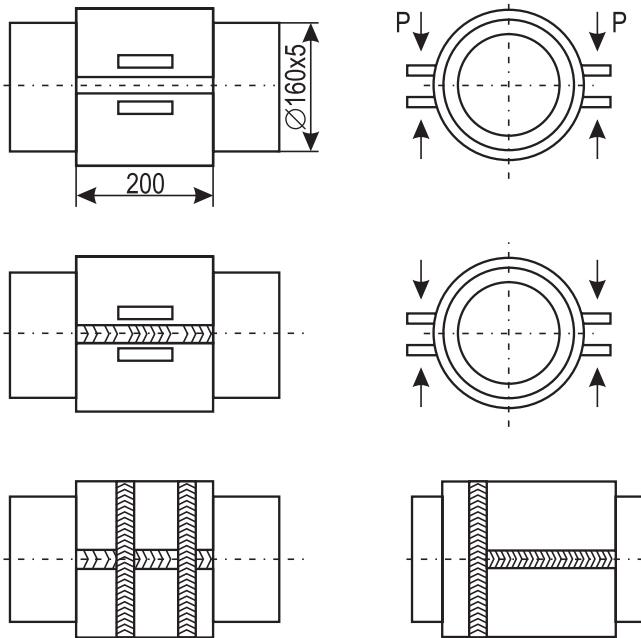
Схемы сборки и сварки моделей бандажного соединения
